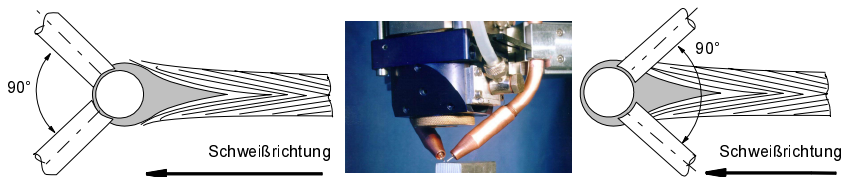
Laserstrahlschweißen mit zwei Zusatzdrähten in „V-Anordnung“, schleppend („± 45°“, links) und stechend („± 135°“, rechts) zur Vorschubrichtung. Mitte: Bearbeitungskopf.
